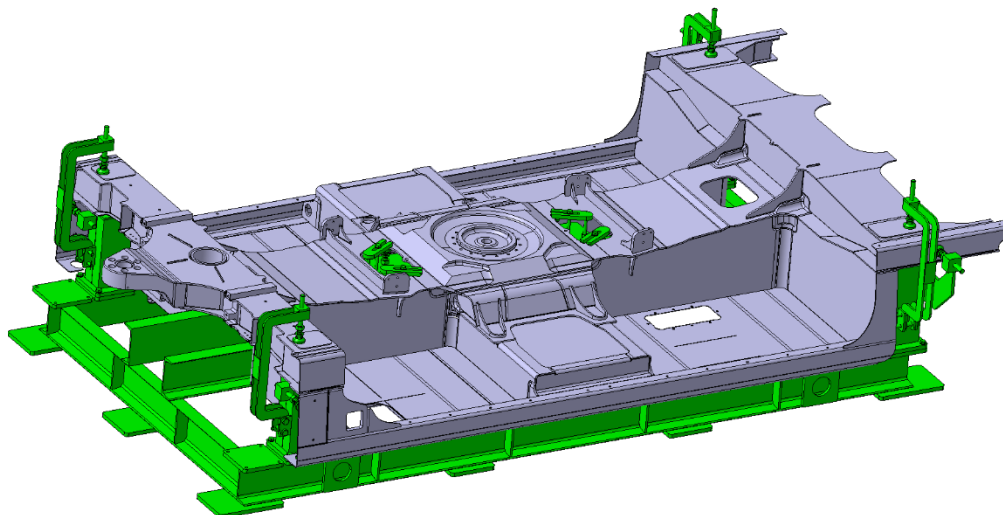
Celý přípravek – rozmístění pro menší obrobek
